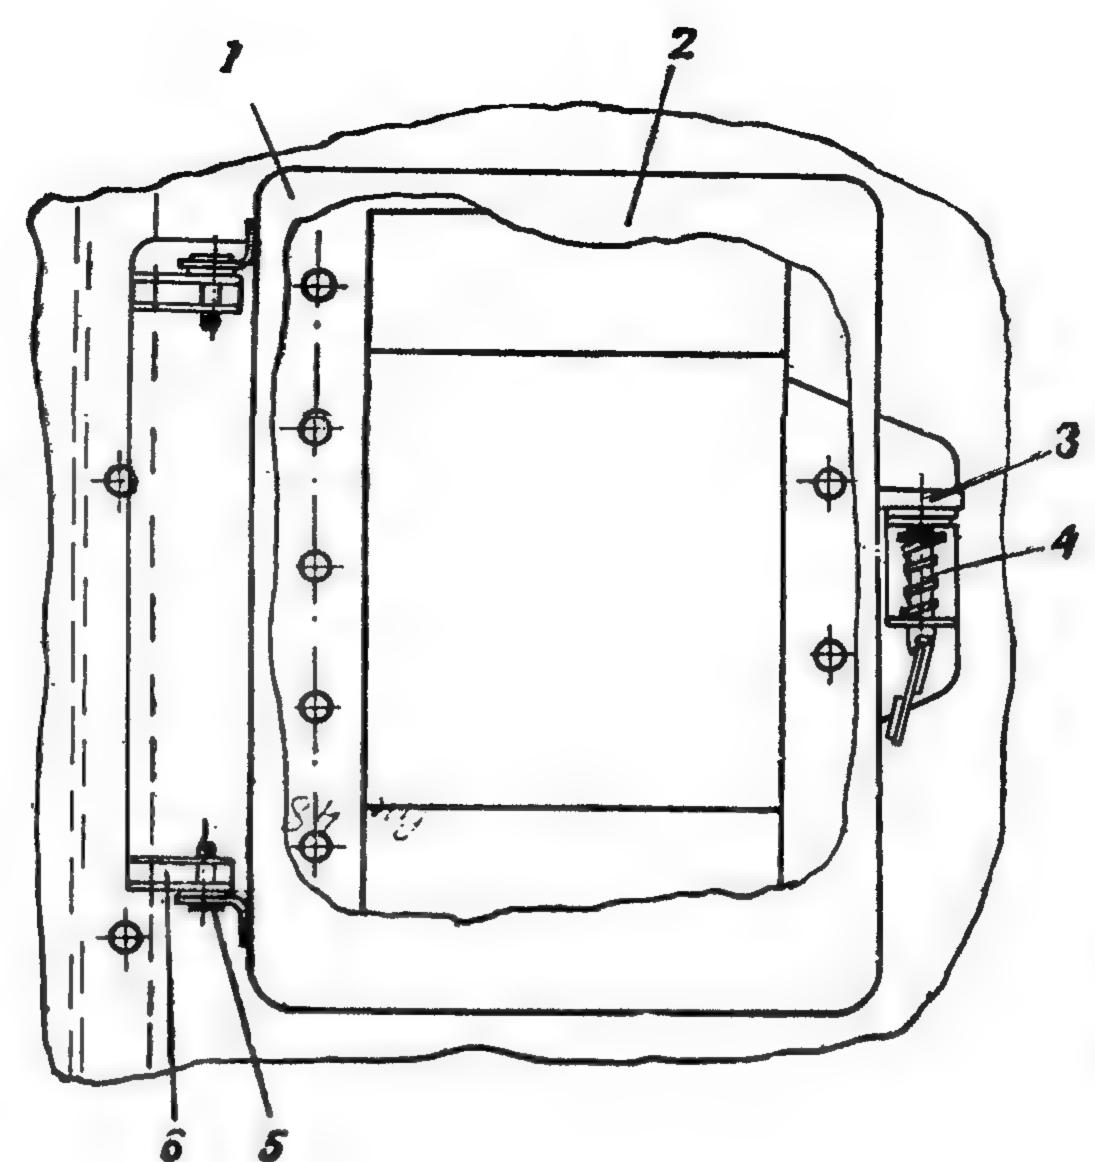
Коробка для укладки прибора ТНПО-170А:
